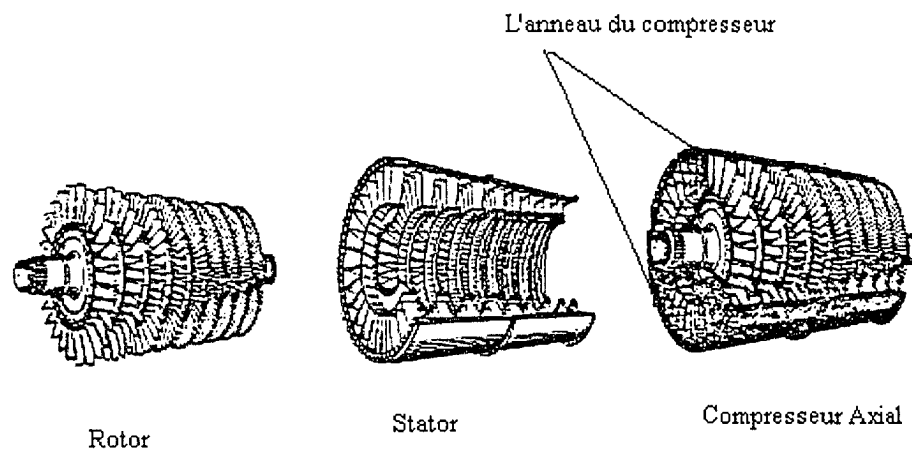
Éléments constitutifs et ensemble du compresseur axial [2]
